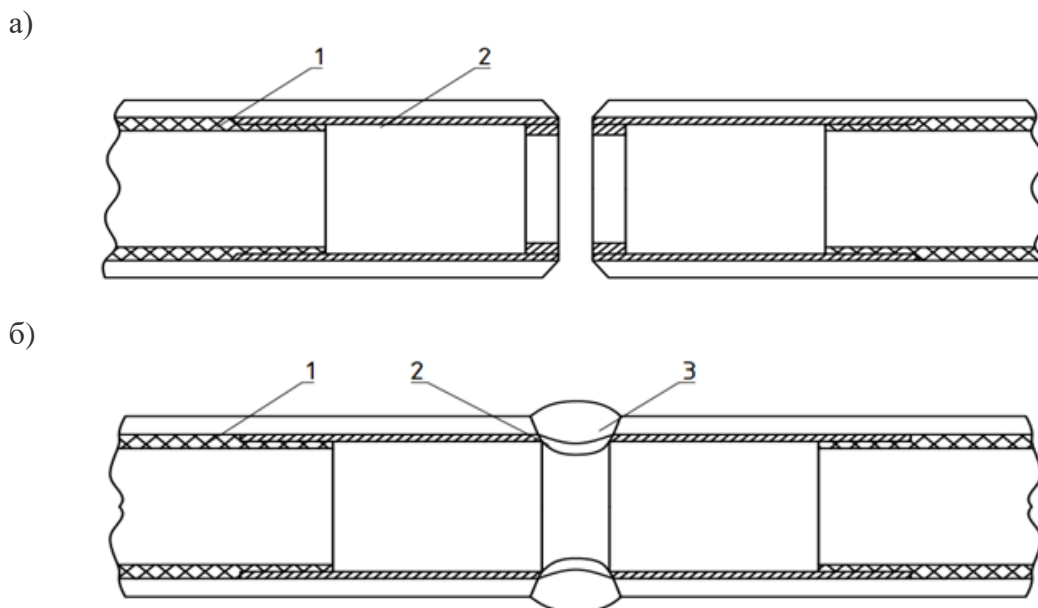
Конструкция внутреннего полимерного покрытия труб с металлизацией концевых участков нержавеющей сталью: а) сверху – концы трубы до сварки; б) внизу – концы трубы после сварки; 1 – полимерное покрытие; 2 – металлизационное покрытие; 3 – слой сварочных шлаков
